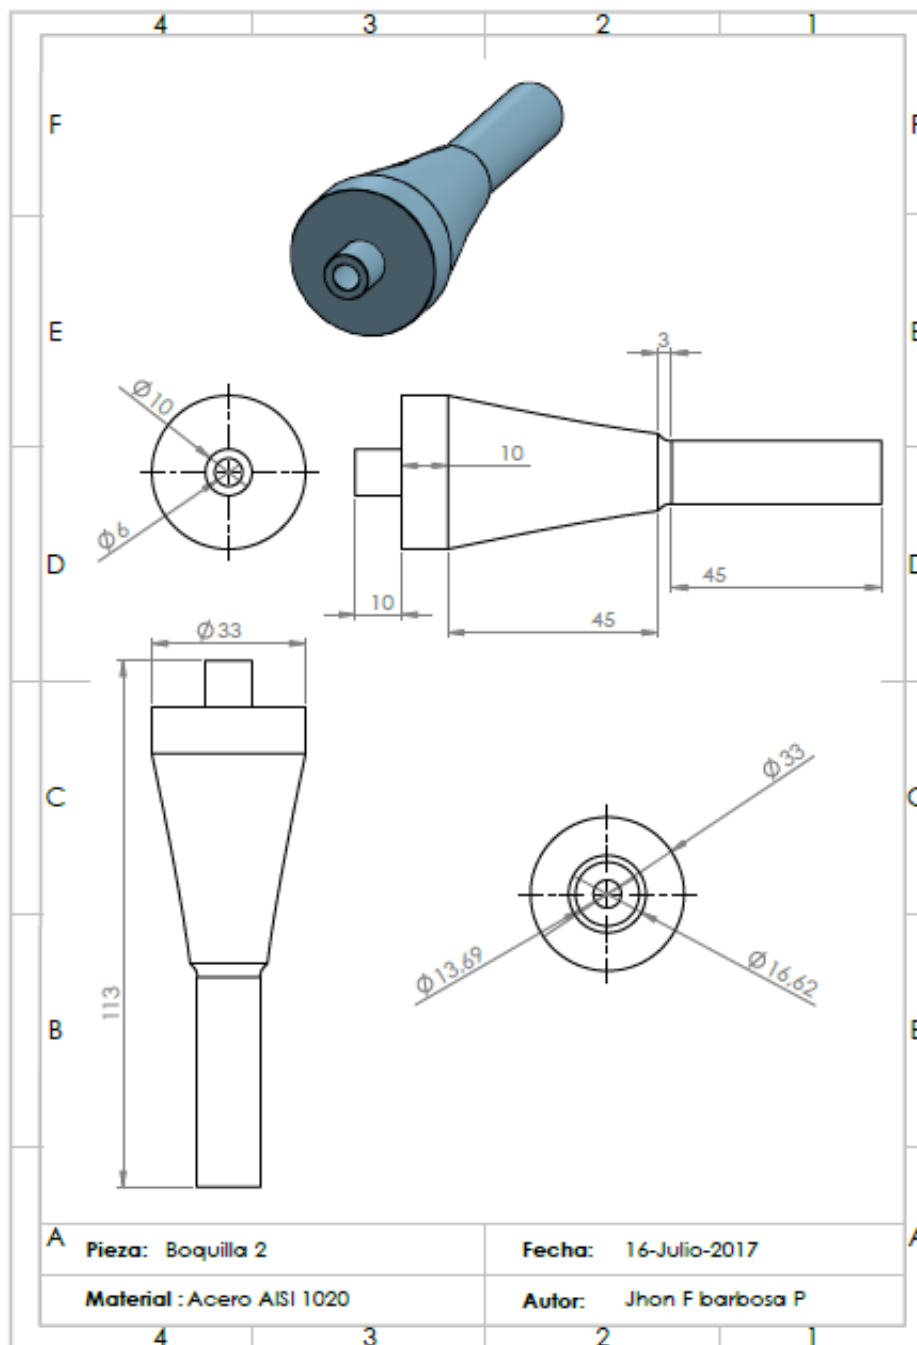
Plano de parte 2 de la boquilla de extrusión.
